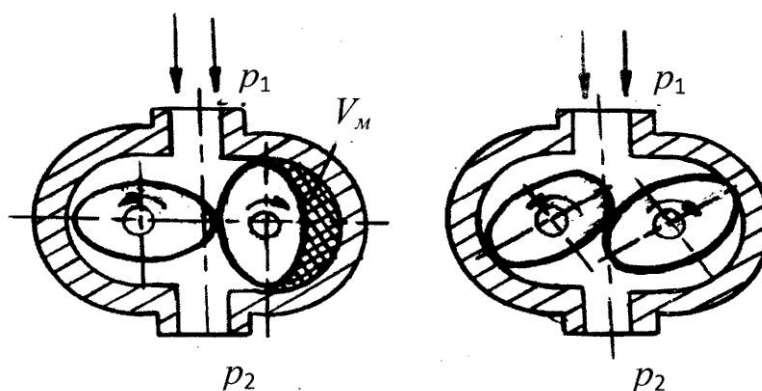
Камерный счетчик с овальными шестернями
